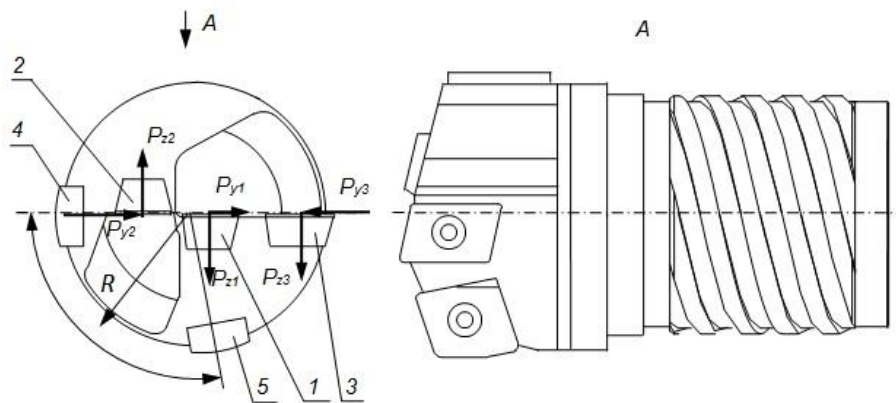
Схема нагружения головки для глубокого сверления отверстий
